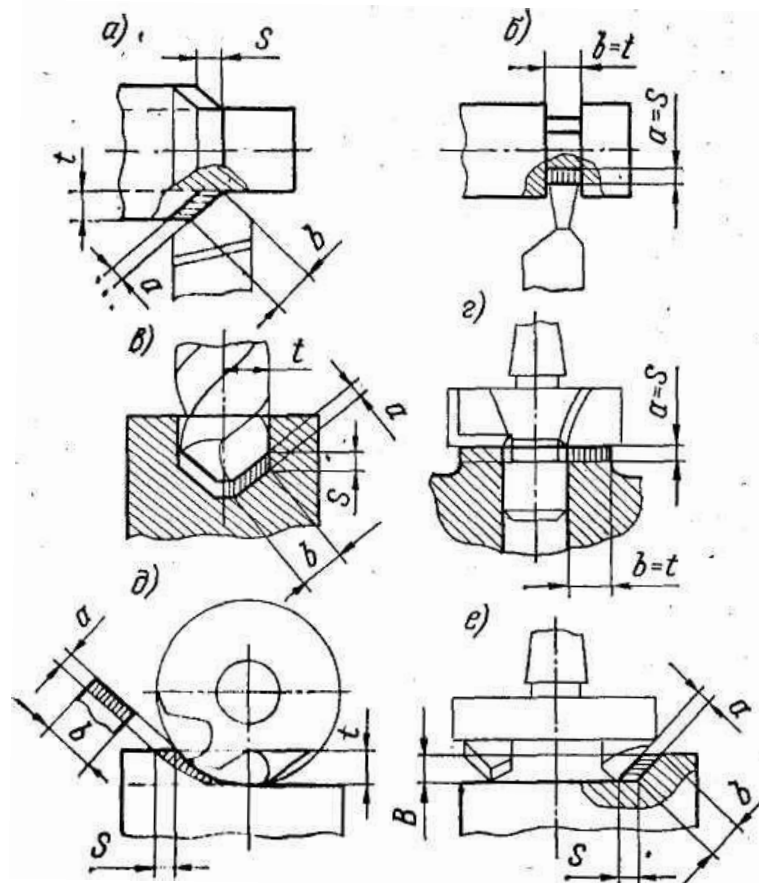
Форма і розміри шару, що зрізається, при обробці деякими видами інструментів:
